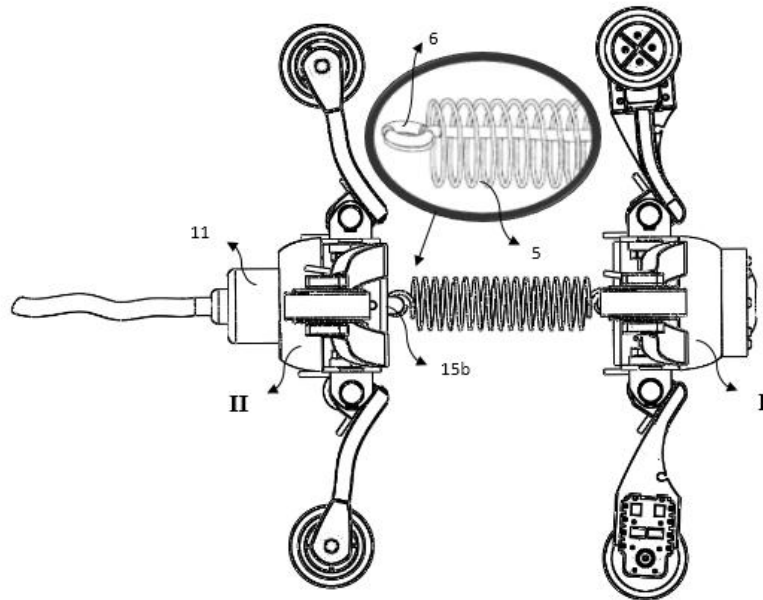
Diseño CAD del robot. (Vista lateral izquierda)
